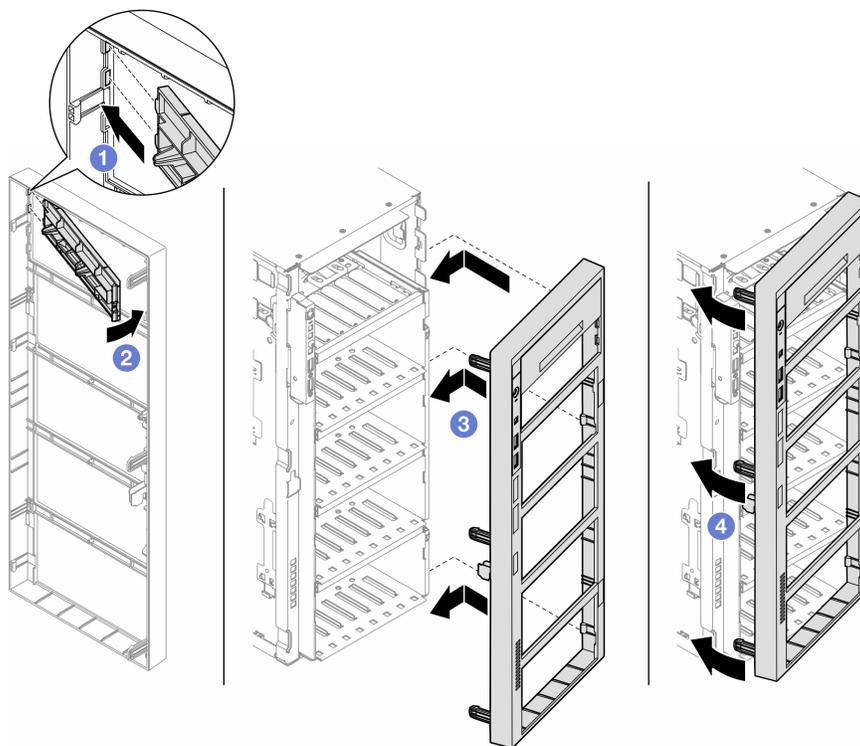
Installation einer Abdeckung der Abdeckblende für eine Laufwerkposition und anschließend einer Frontblende
